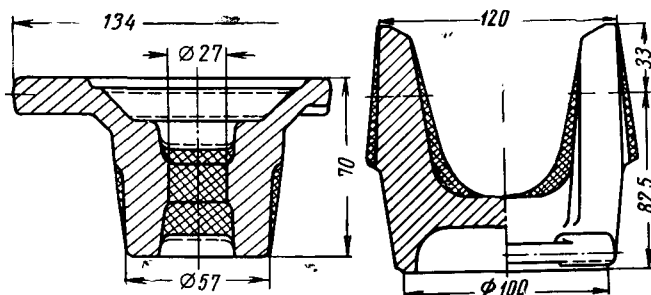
Поковка фланца вторичного вала (заштрихованная область — штамповка на молоте; без штриховки — штамповка на КГШП)
